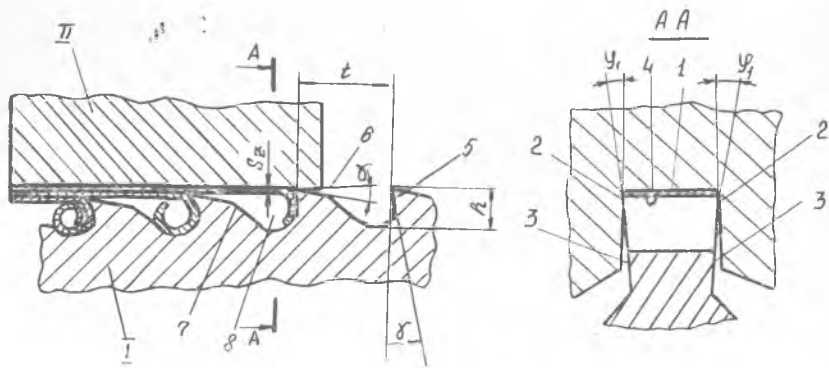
Схема резания и элементы зуба протяжки; 1 — протяжка; II — обрабатываемая деталь;  $S_z$  — подача на зуб
